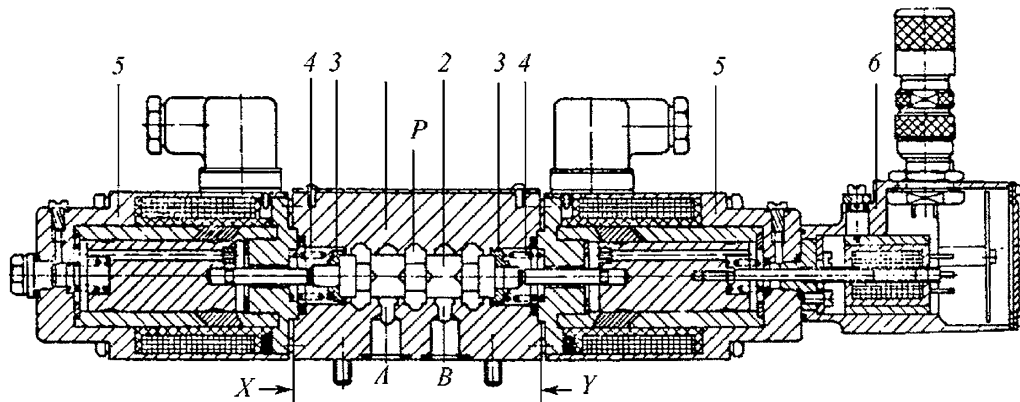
Четырехлинейный распределитель с управлением ПЭМ и электрической обратной связью: 1 — корпус золотника; 2 — золотник; 3 — подвижные шайбы; 4 — центрирующие золотник пружины; 5 — корпус левого и правого ПЭМ; 6 — датчик обратной связи (обозначения каналов см. на рис. 4.6)
